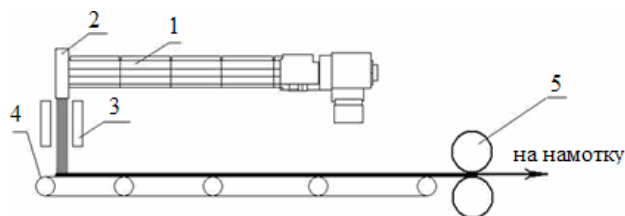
Загальний вид машини з виготовлення фільтрувального матеріалу: 1 – екструдер; 2 – формуюча головка; 3 – витяжний пристрій (головка з гарячим повітрям); 4 – приймальний пристрій (конвеєр); 5 – намотувальний барабан
